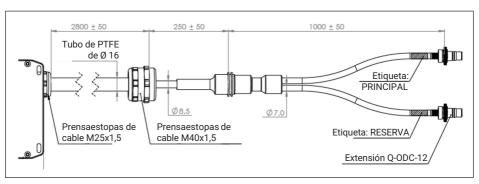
Dibujo técnico de la caja de interconexión – lado de la caja (dimensiones en mm)
